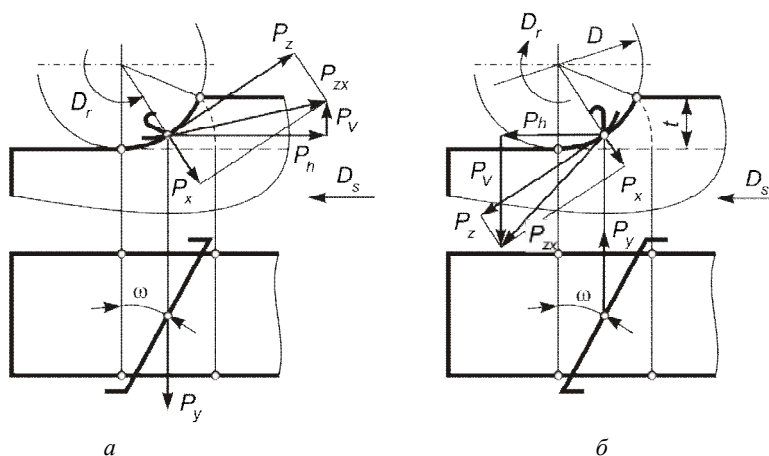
Силы на зубе цилиндрической фрезы при встречном (а) и попутном (б) фрезеровании
